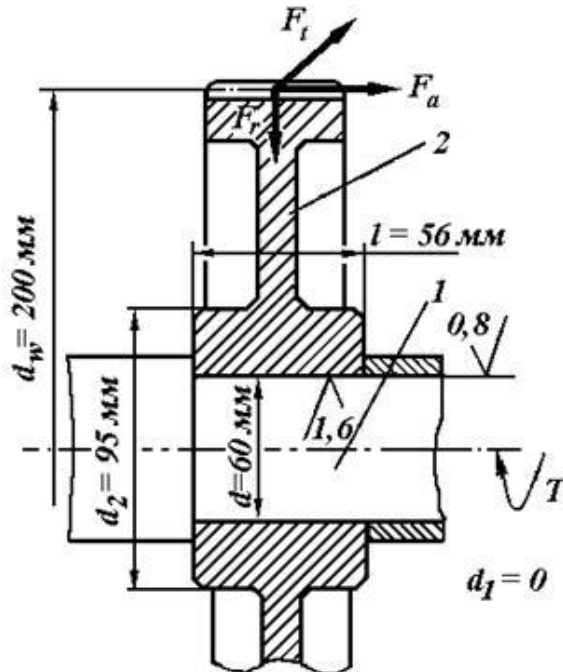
Зубчатое колесо, установленное на вал запрессовкой
